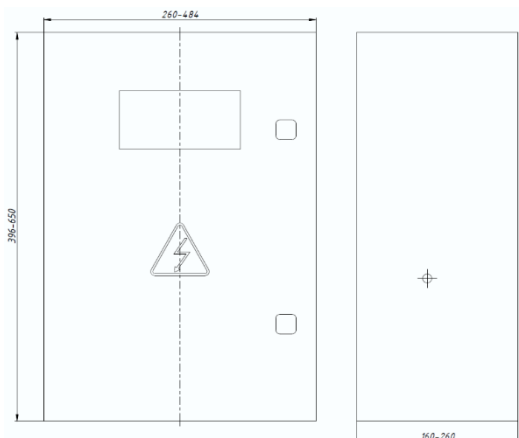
Общий вид и габаритные размеры шкафов с одним счётчиком в пластиковом корпусе.
